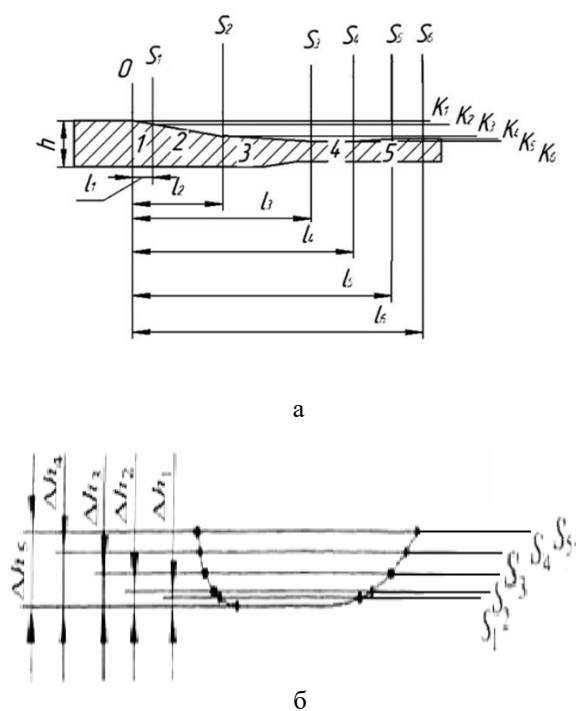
Схема перемещения заготовки (гильзы): а – в осевом, б – в радиальных направлениях
